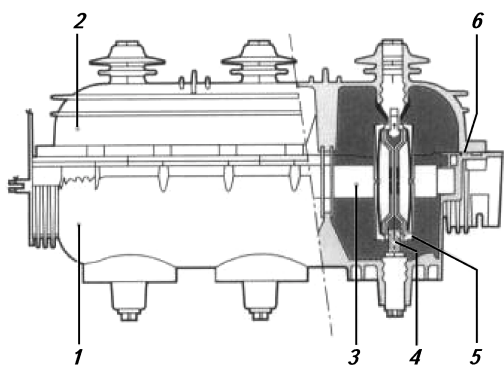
Элегазовый выключатель нагрузки: 1 – корпус; 2 – крышка; 3 – вал привода; 4 – неподвижный контакт; 5 – подвижный контакт; 6 – уплотнение
